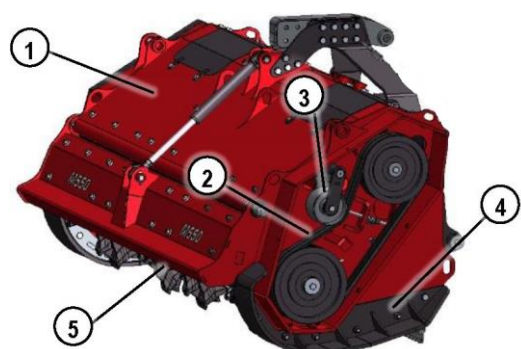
Мульчирующая фреза со снятой коробкой передач
